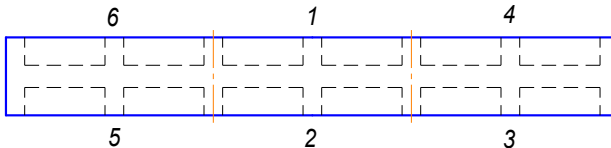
Одночасна обробка поверхонь нежорстких деталей з двох боків
